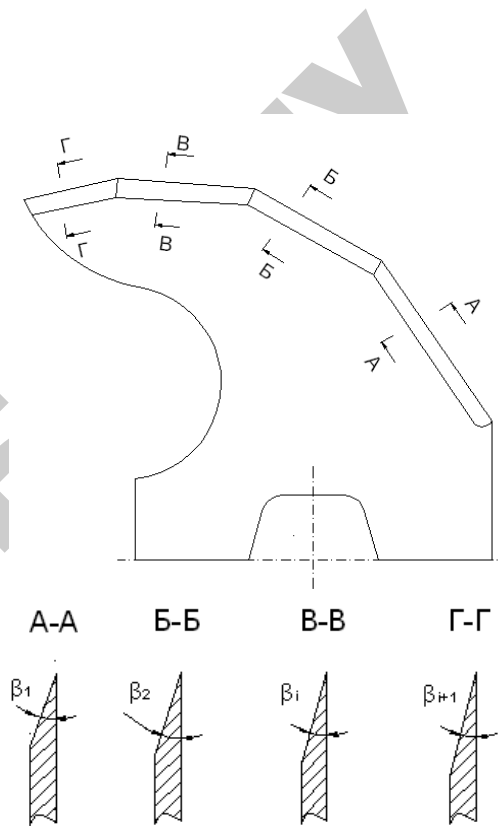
Схема куттерного ножа с изменяющимся углом заточки режущей кромки
